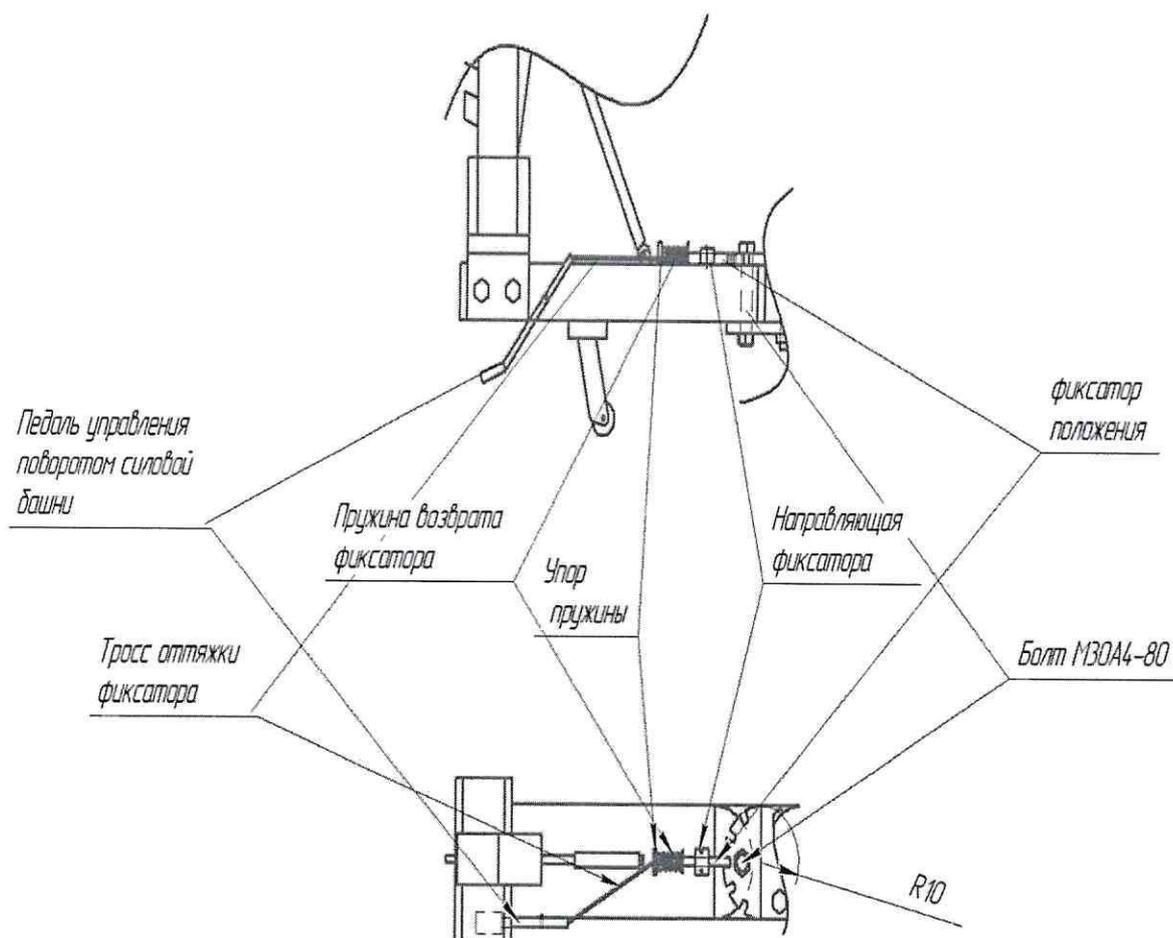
Принципиальная схема устройства поворотного механизма силовой башни стапеля с ножным управлением
